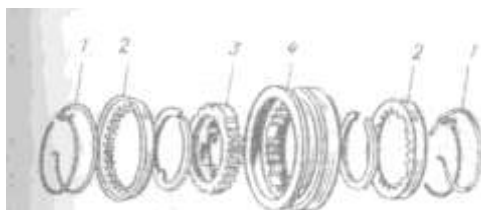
Деталі і схема синхронізатора коробки передач (ВАЗ-2105):
